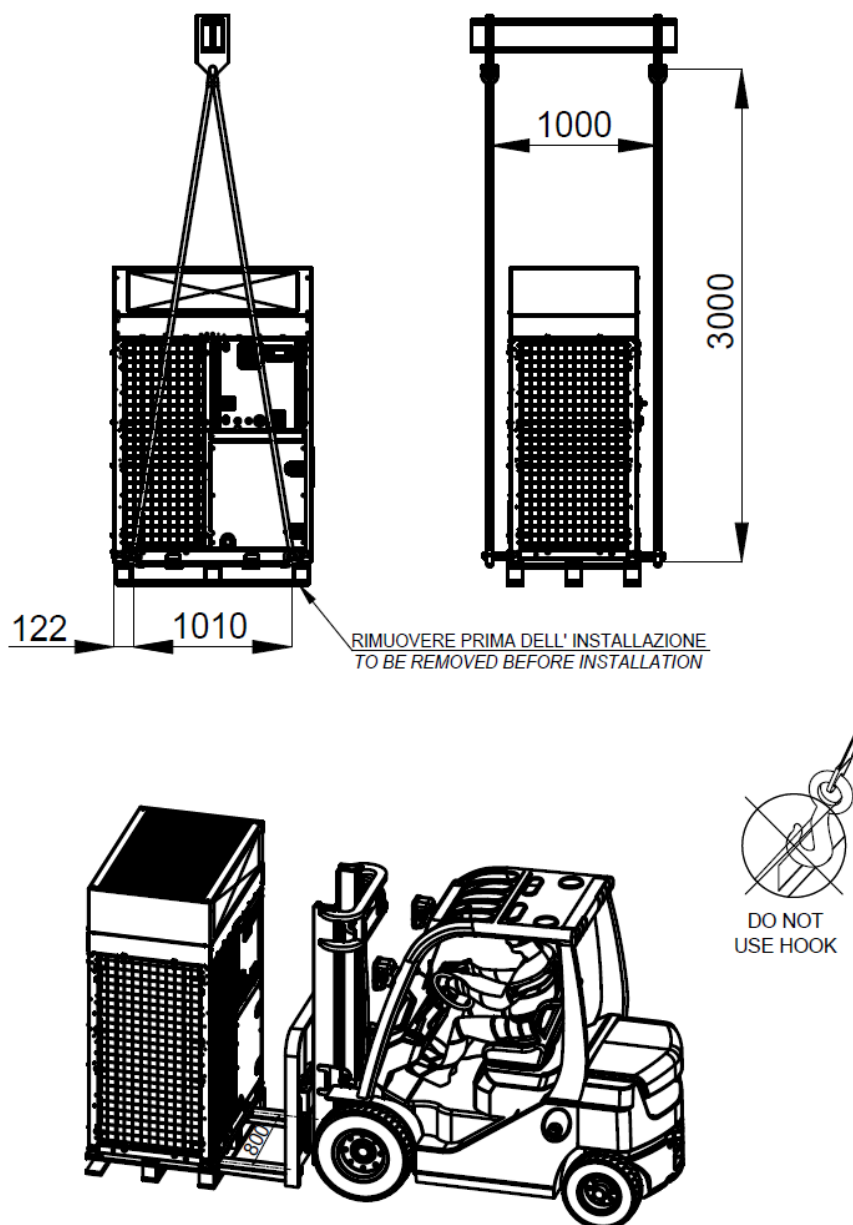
Instrucciones de aparejo con carretilla elevadora
